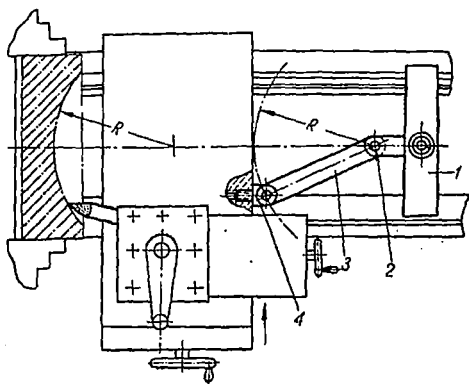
Приспособление для обработки вогнутых наружных сферических поверхностей больших радиусов.
